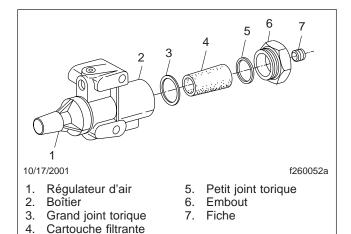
, Composants du filtre ou régulateur d'air de la boîte de vitesses Eaton Fuller
